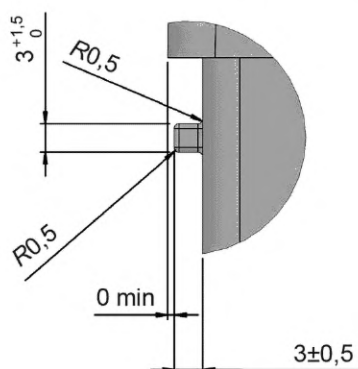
Размеры выступа для ЗПО (деталь V), приведенного на рисунке 23
